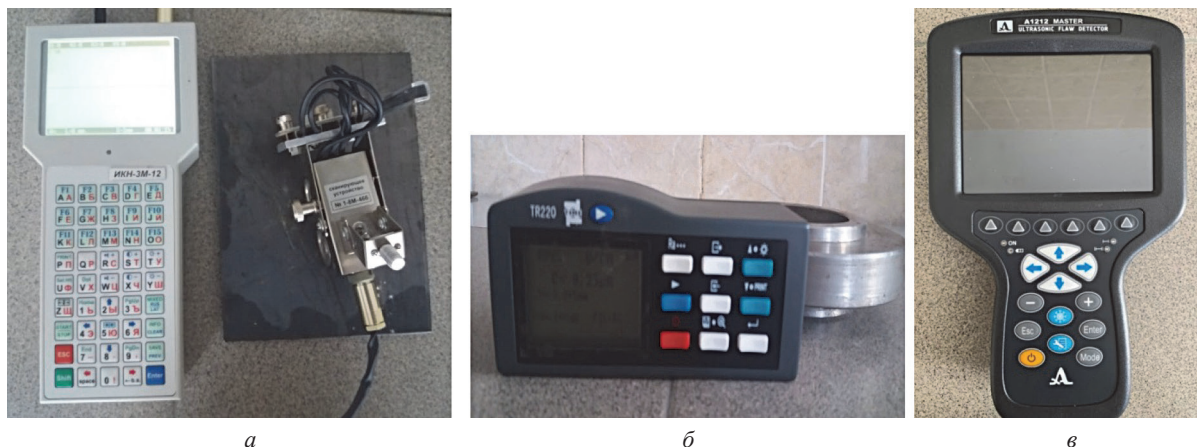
Приборы, использованные в исследованиях отливок: а – измеритель концентрации напряжений ИКН-3М-12; б – прибор для измерения шероховатости TR-220; в – ультразвуковой дефектоскоп А1212 Master
